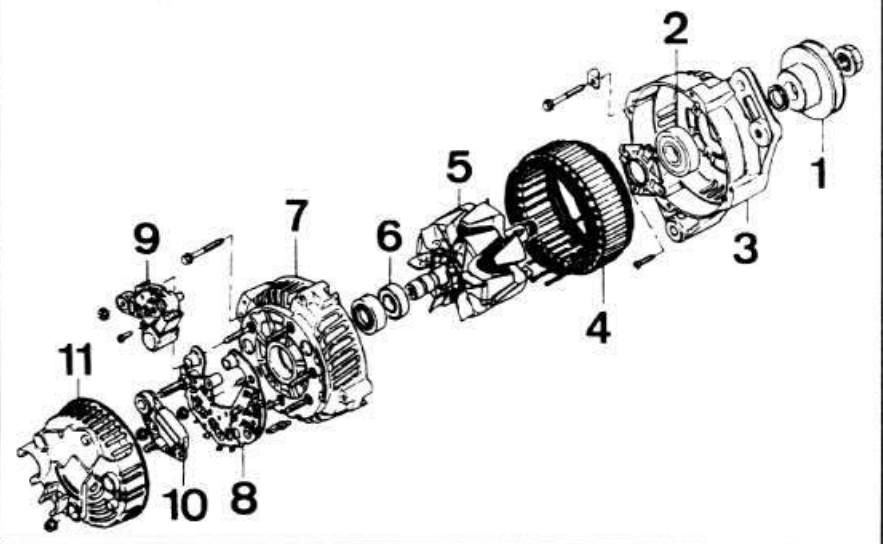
Детали генератора автомобилей с дизельными двигателями: 1—шкив; 2—подшипник со стороны привода; 3—крышка со стороны привода; 4—статор; 5—ротор; 6—подшипник со стороны контактных колец; 7—крышка со стороны контактных колец; 8—выпрямительный блок; 9—щеткодержатель; 10—регулятор напряжения; 11—защитный кожух
